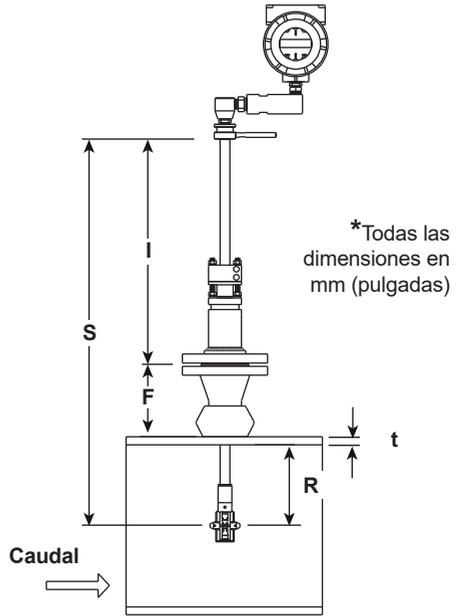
Cálculo de inserción (medidor si herramienta de inserción)
